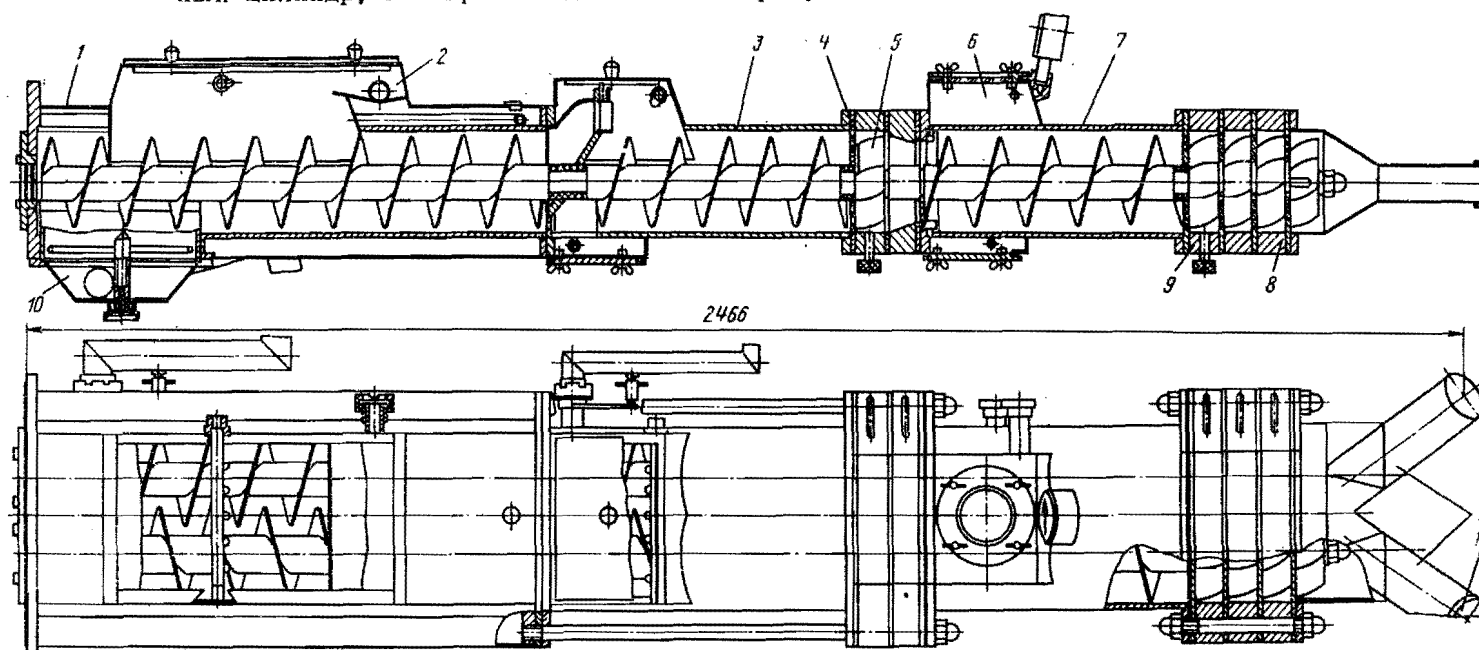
Общий вид шнекового текстуратора маслоизготовителя марки А1-ОЛО/1:
